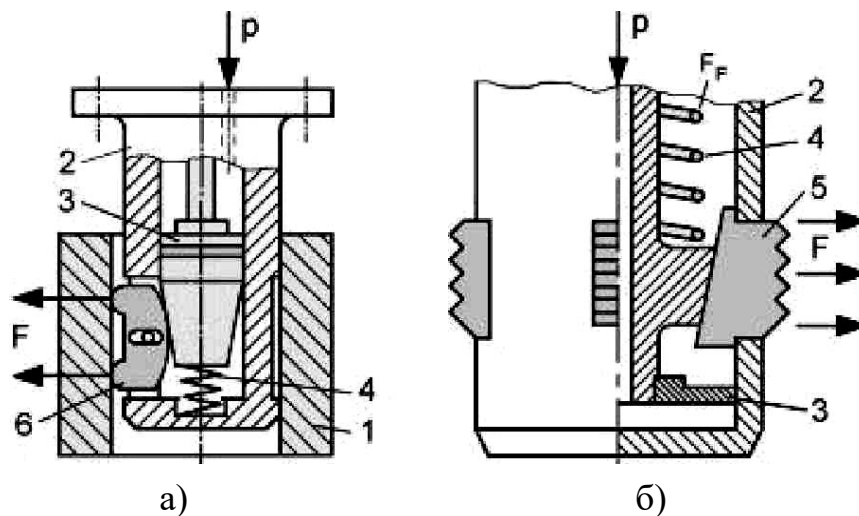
Конструкції ЗП для затиску деталей за внутрішню поверхню:
